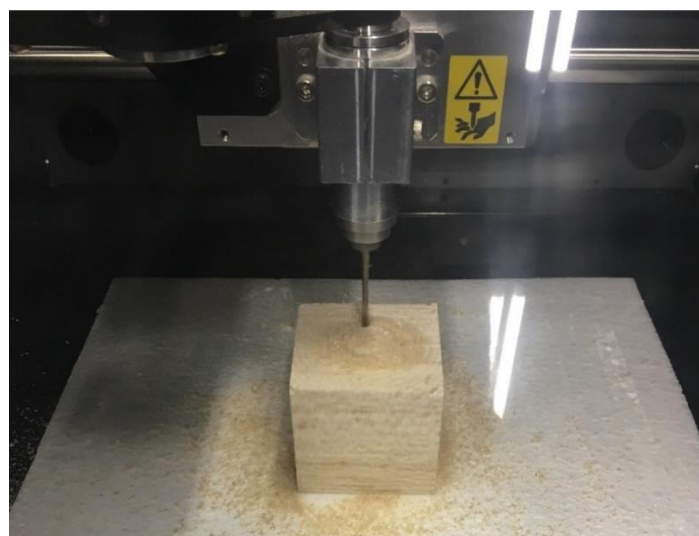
Maquinado Fresadora CNC – Inicio de maquinado
